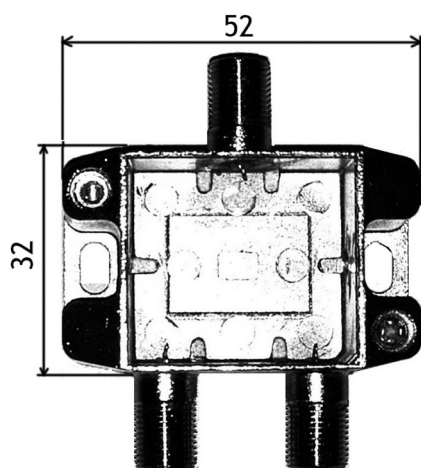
Внешний вид подготовленного корпуса от сумматора типа Premier 4-930 (размеры "колодца" для монтажа: 30x32 мм, глубина 13 мм)
